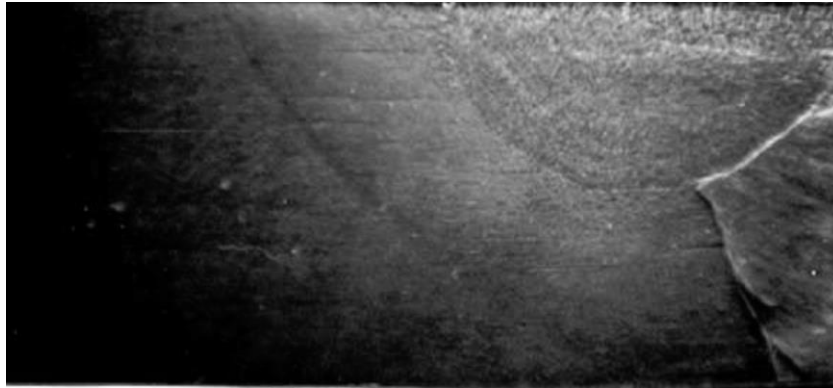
macrographie de la soudure avec une 3ème réparation (R3)
